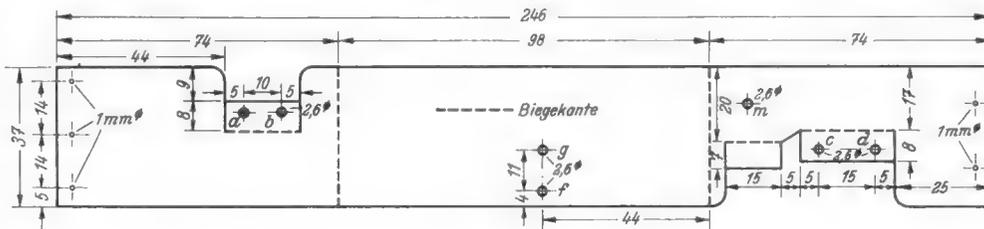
Chassisblech (Aluminiumblech 0,5 mm). Löcher ohne Maßangabe = 2,5 mm Ø
